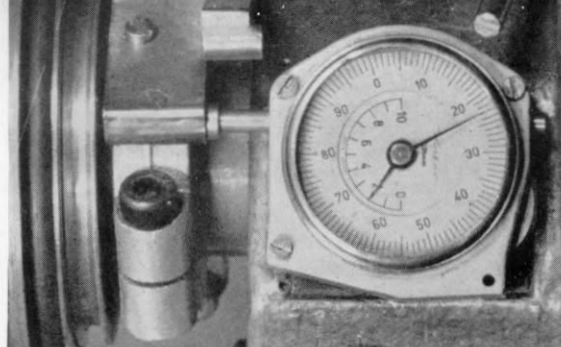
Detailansicht der fertig eingebauten Meßuhr.
